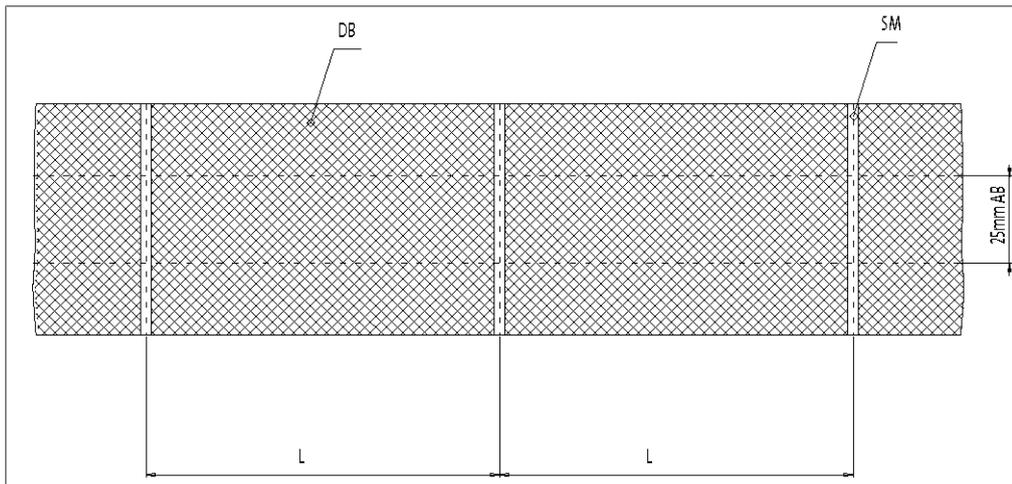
Etikettenzeichnung für Schnittmarkengeometrie mit transparenter Schnittmarke
